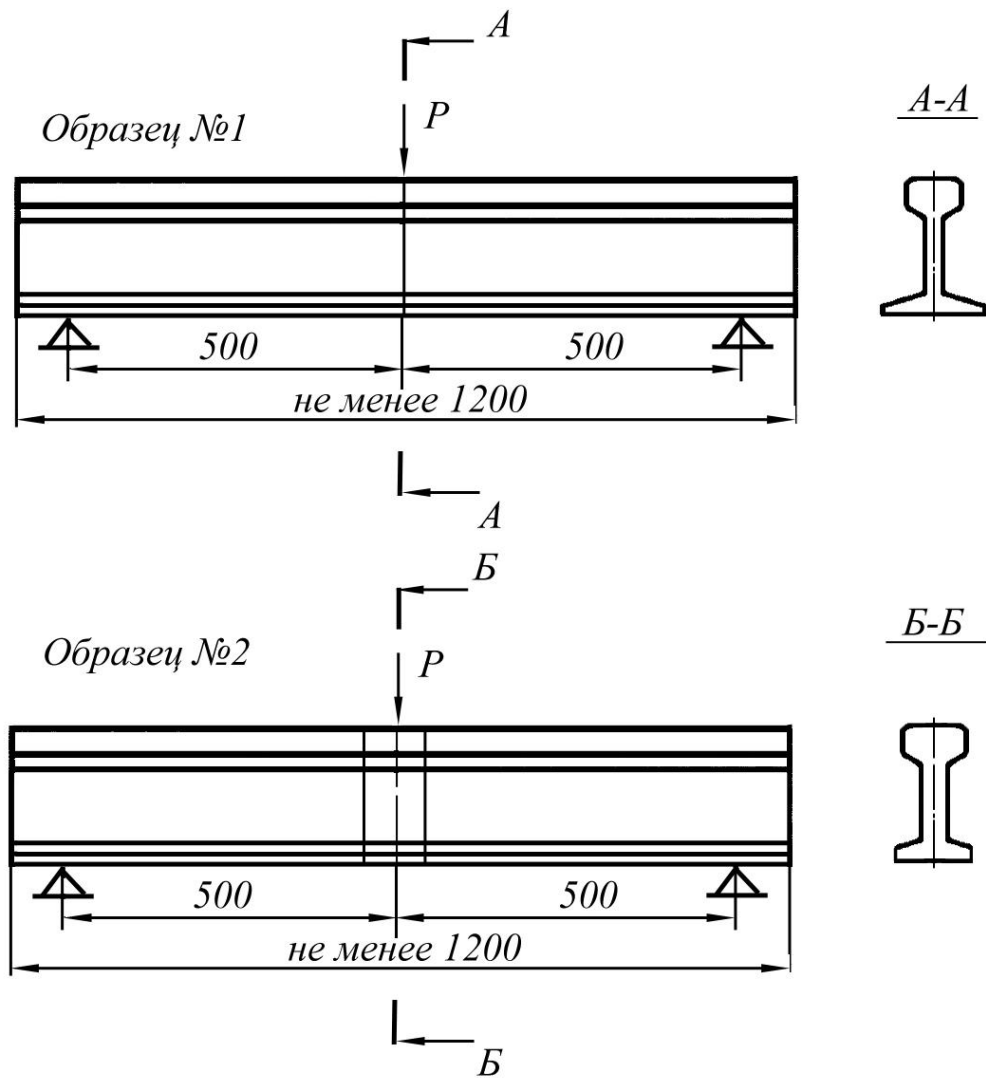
Конструкция и размеры сварных образцов
